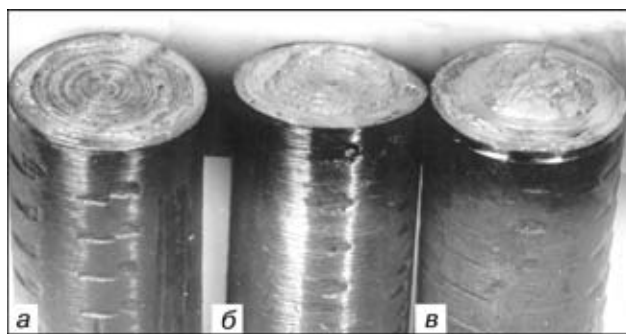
Поверхности изломов сварных соединений, полученных при давлении нагрева 25 (а), 40 (б), 50 МПа (в)
